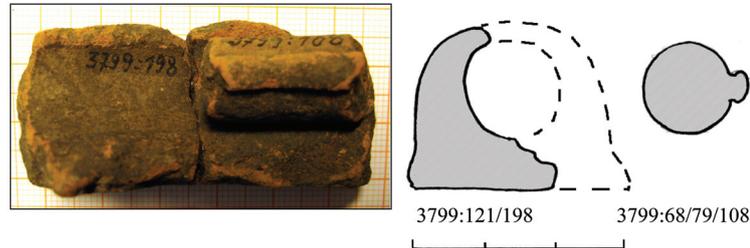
Hohlringgussform und tönerner Gusskern aus Asva A/C.
